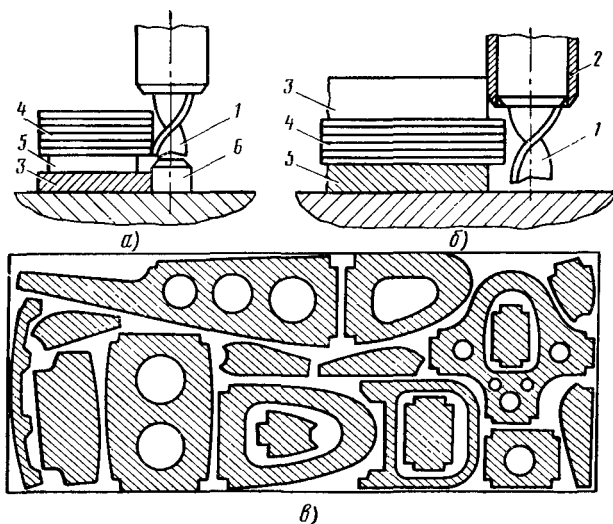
Вырезка заготовок и деталей фрезерованием:
